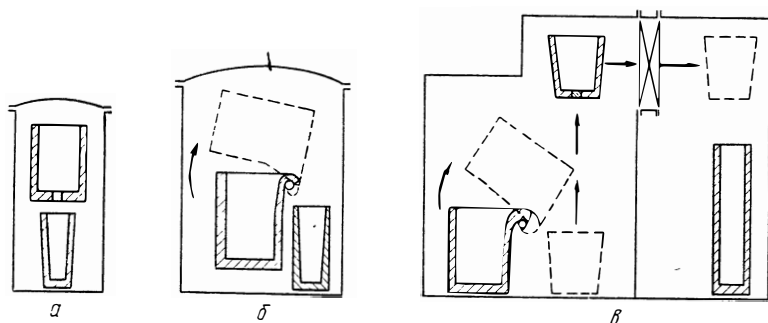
Типы конструкций вакуумных установок для плавки и разливки металлов [4]:
